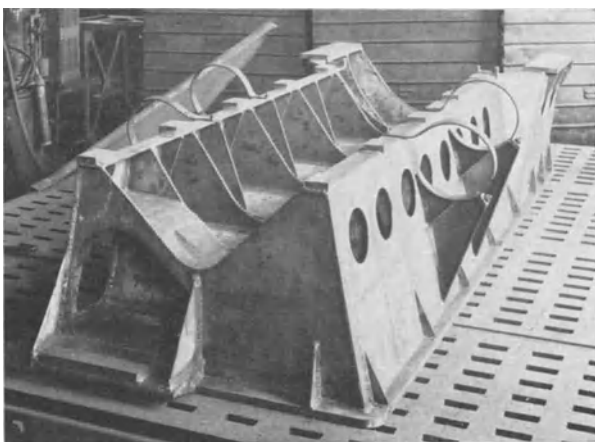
Geschweißtes Dieselmotorengestell.
